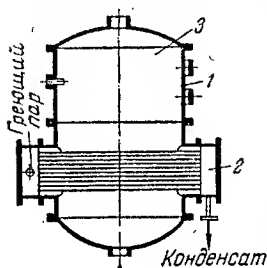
Выпарной аппарат с горизонтальной трубчатой нагревательной камерой и вертикальным цилиндрическим корпусом:
